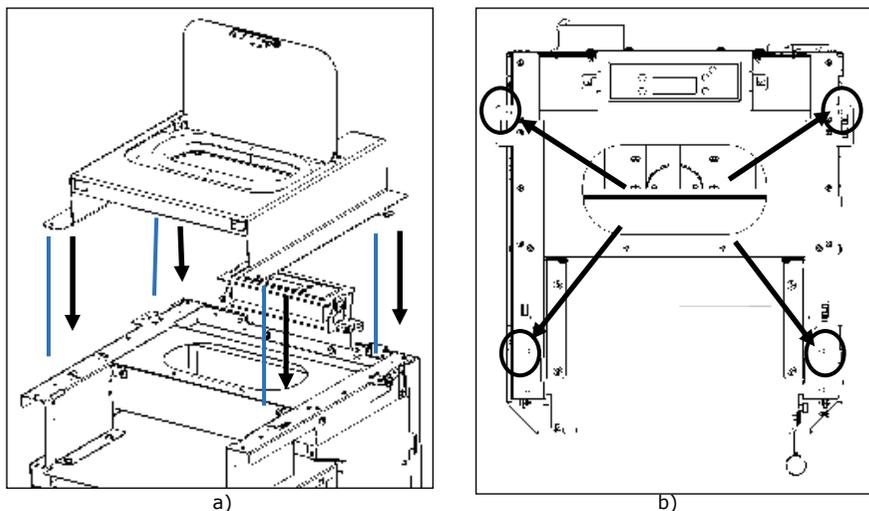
Posizionare il coperchio sulla struttura apparecchiature
